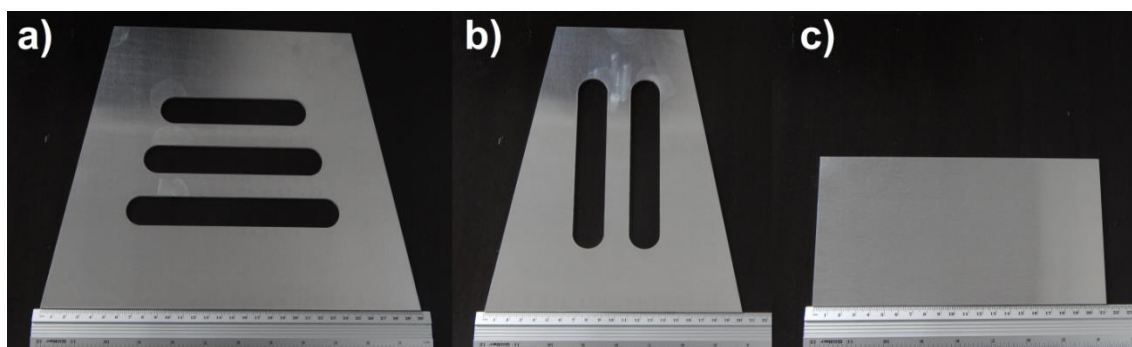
11 Placas de alumínio, detalhes do corte a laser para construção do atenuador de impacto.
